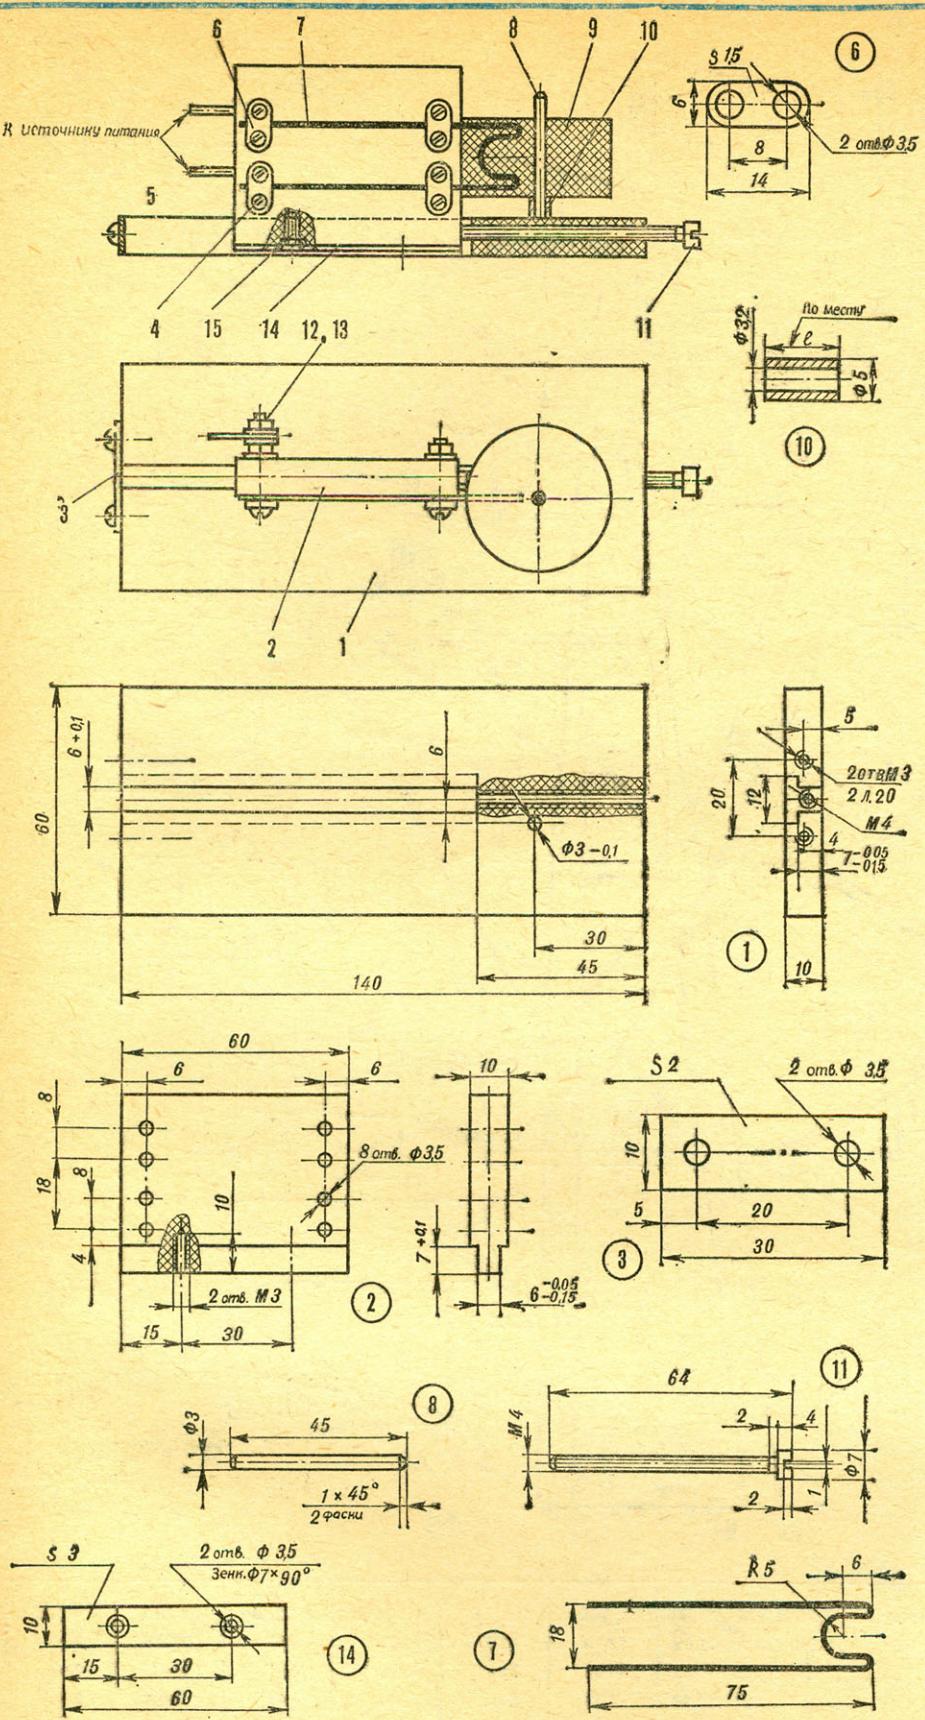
Приспособление для обработки заготовок гребных винтов:
